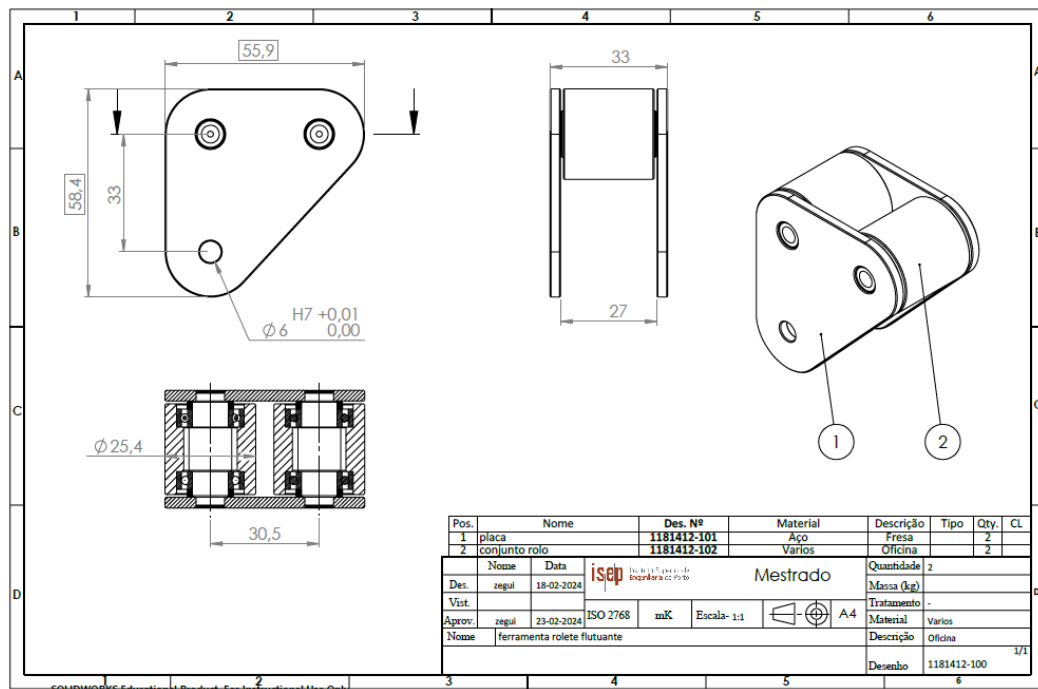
Desenho de conjunto da ferramenta para o ensaio de rolete flutuante
